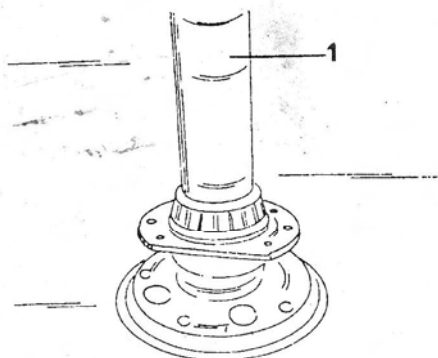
Запрессовка подшипника на полуоси. Труба для запрессовки должна иметь соответствующую длину.
